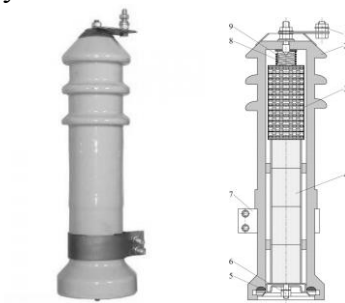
Вентильный разрядник РВО-10У1: 1, 6 – контактные болты; 2 – корпус разрядника; 3 – блок искровых промежутков; 4 – вилитовые диски; 5 – резиновая прокладка; 7 – крепежный хомут; 8 – полоска фольги; 9 – пружина
